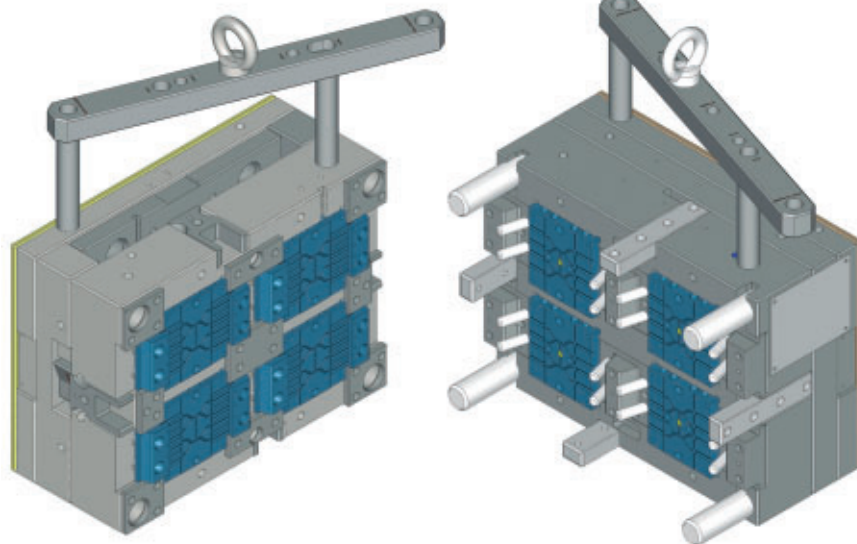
Auf einen Produktentwickler kommen bei Blum mehr als zwei Betriebsmittelkonstruktoren, die unter anderem Werkzeuge für den Zinkdruckguss und den Kunststoffspritzguss entwickeln.
